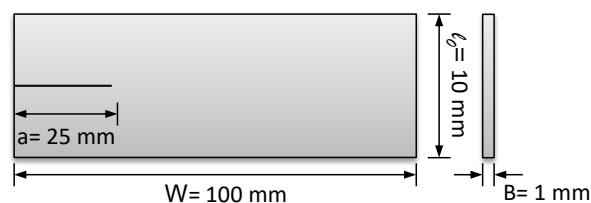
Configuración *pure shear* con dimensiones de las probetas de fractura.
